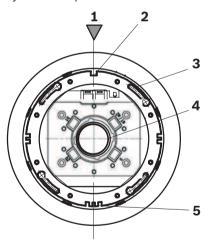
Fixation du socle au boîtier arrière pour montage au plafond
